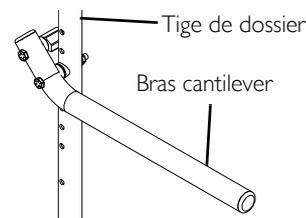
Utilisation des bras cantilever non-verrouillables
